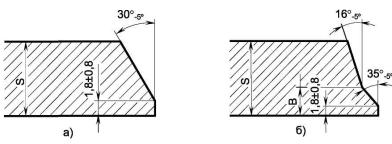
Форма разделки кромок труб для комбинированной сварки с применением Комплекса автоматической сварки
